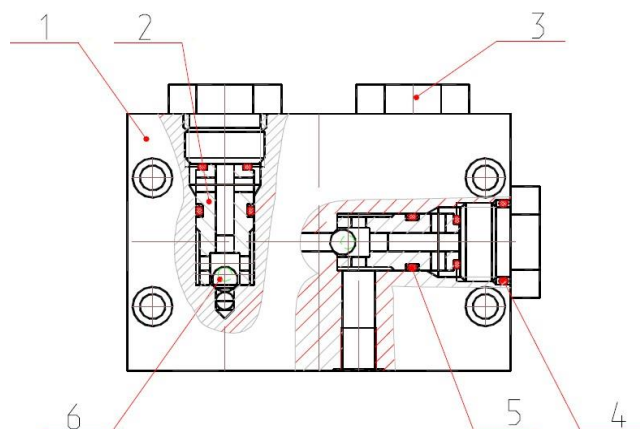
Конструкция пристыкованного клапана «ИЛИ»: 1 – корпус; 2 – втулка; 3 – заглушка; 4, 5 – кольца; 5 – шарик.
